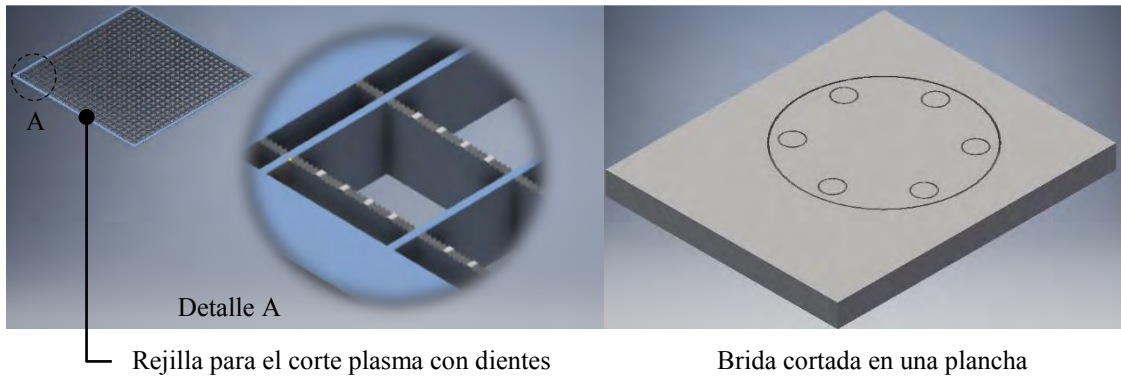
Rejilla de apoyo y plancha de acero
